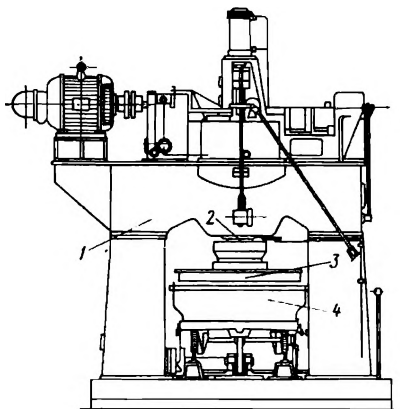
Шлифовально-полировальный станок модели ВШ-3
